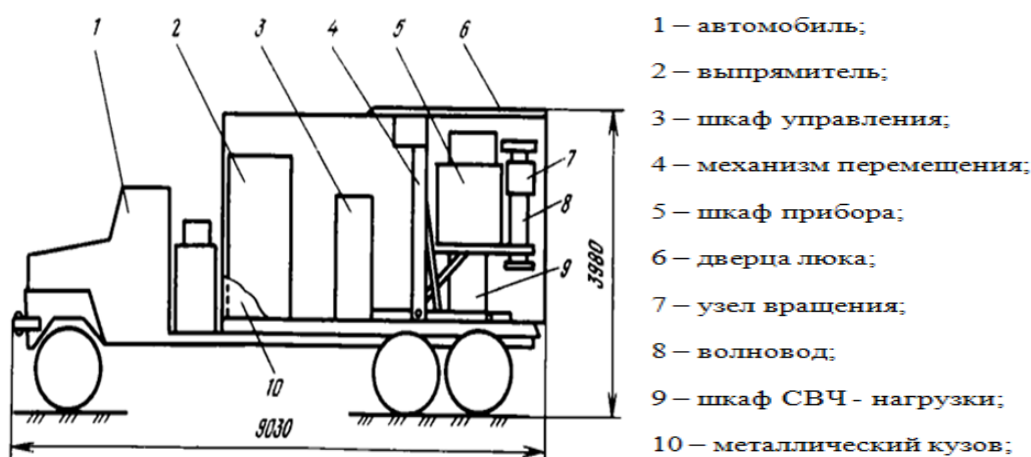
Мобильная СВЧ-установка для изготовления свай ТУГС
